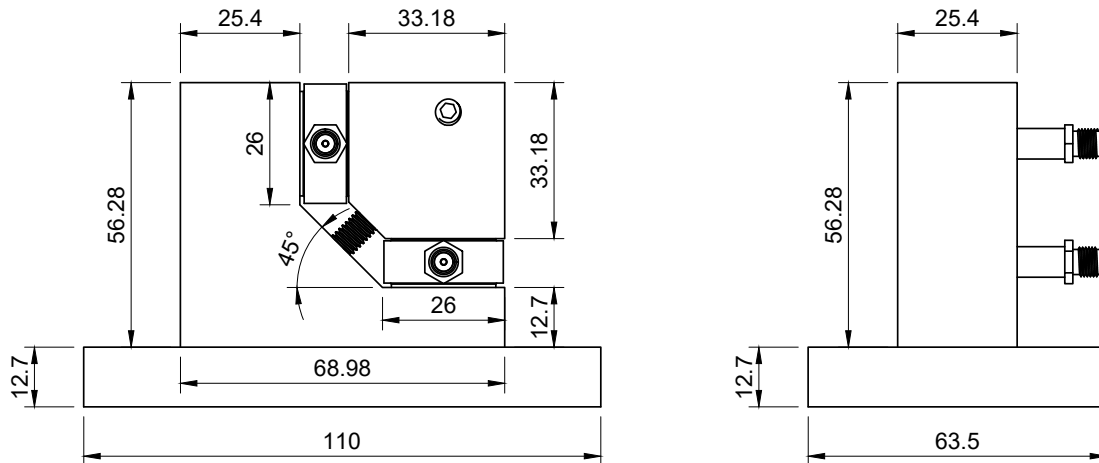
Dimensões em milímetros do sistema de medida de forças biaxial. Fonte: Autor.
